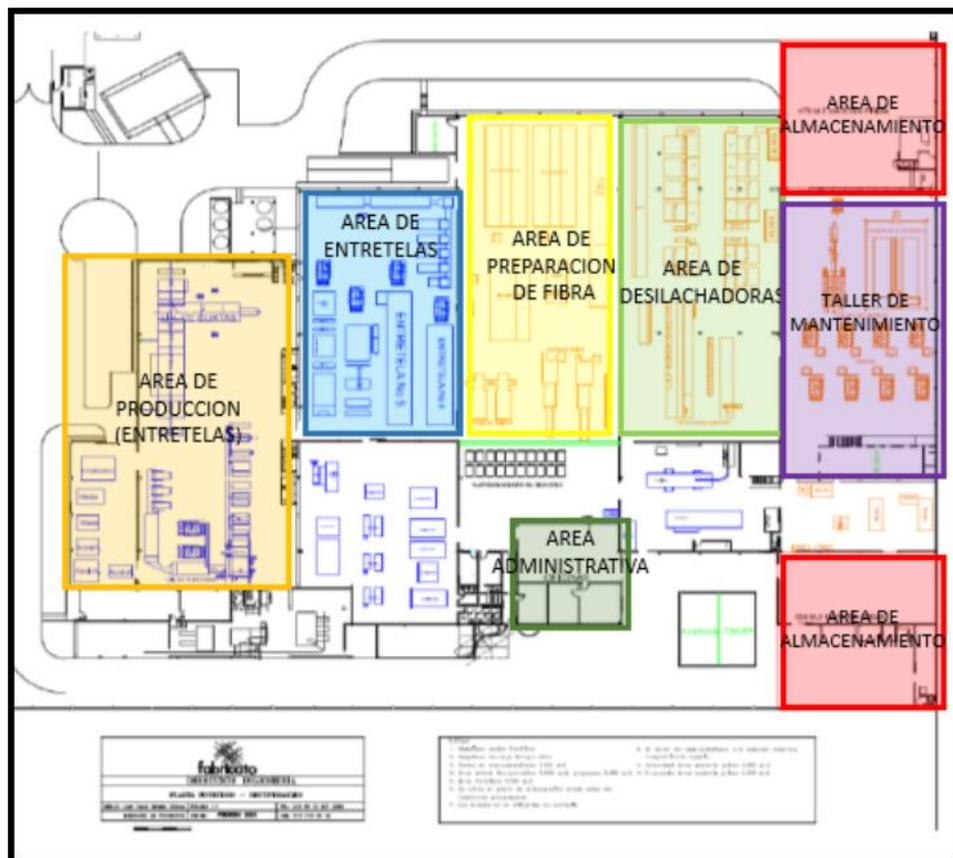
PLANTA DE PROCESO DE PLANTAS DE NOTEJIDOS
